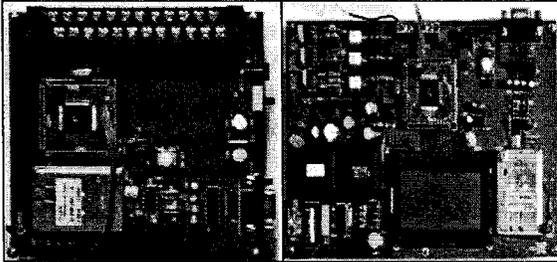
개발된 Control Panel(좌측: 1. 우측: 2)
